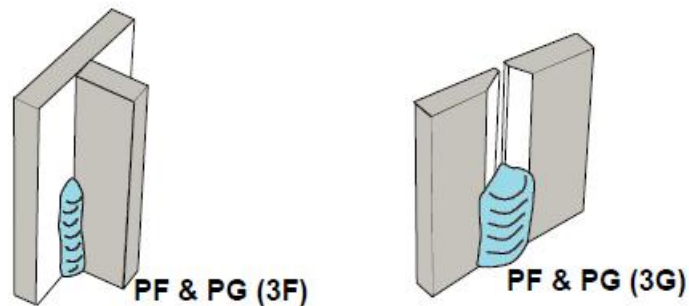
Posições de soldadura do tipo vertical PF e PG
